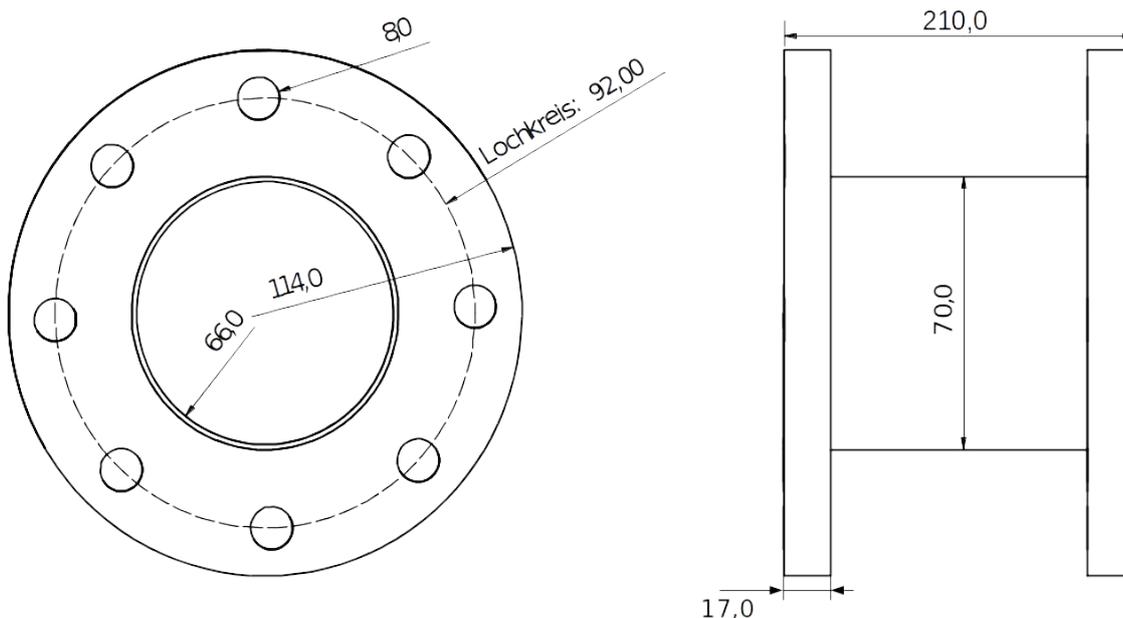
Anschlussmaße vom Gehäuse mit CF Flansch
